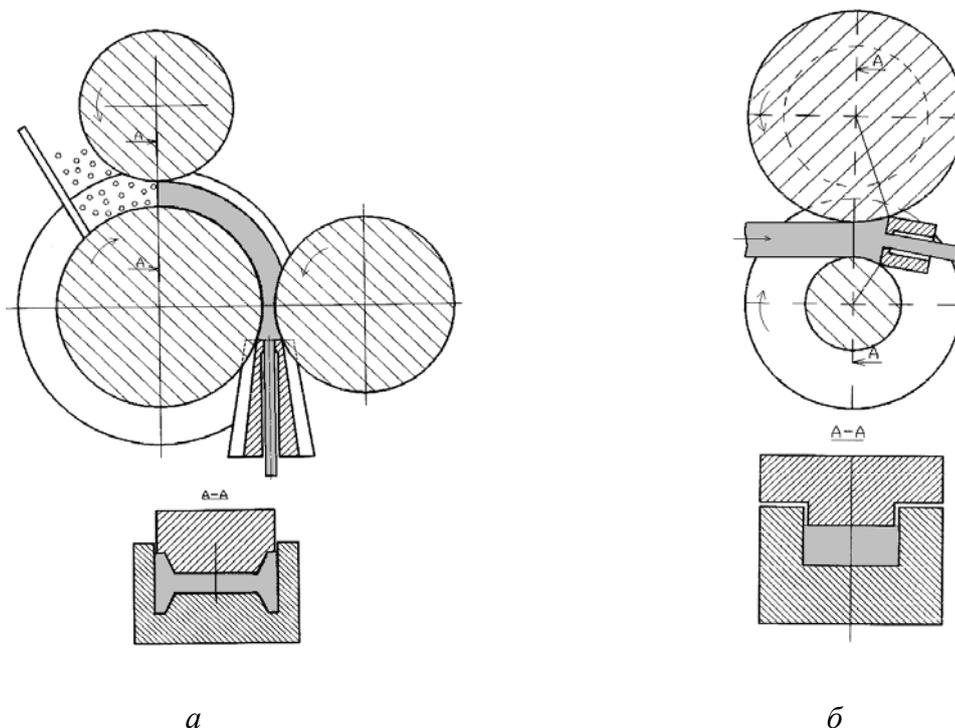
Устройства для получения профилей и проволоки из цветных металлов и сплавов: *а* – из порошковых материалов; *б* – из литой заготовки
